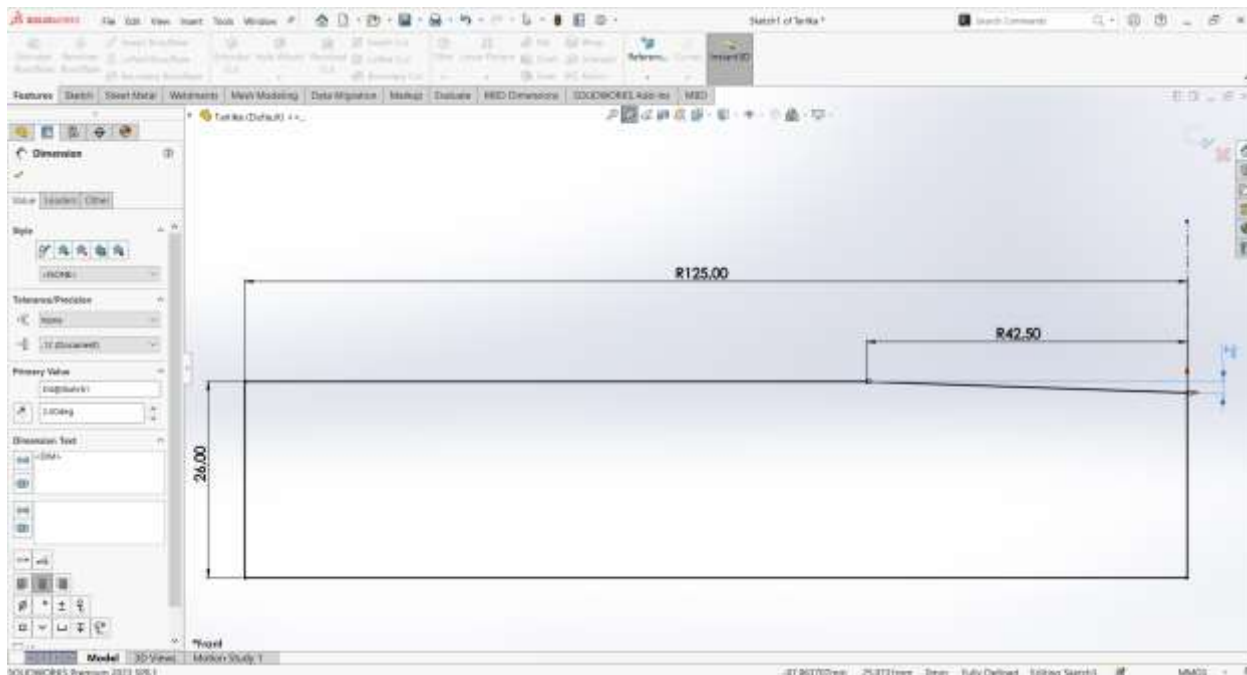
Побудова креслення в режимі ескізу спеціальної платформи для заготовки
